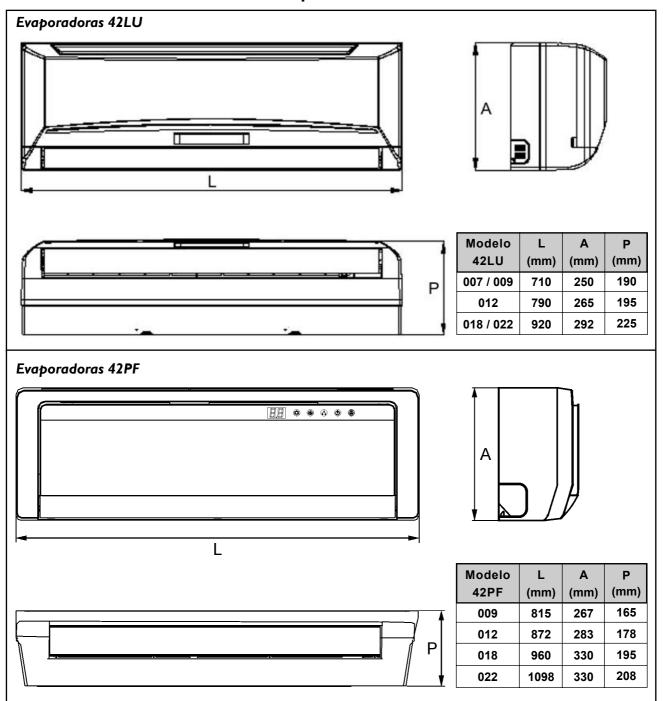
DIMENSIONAL DAS UNIDADES EVAPORADORAS
